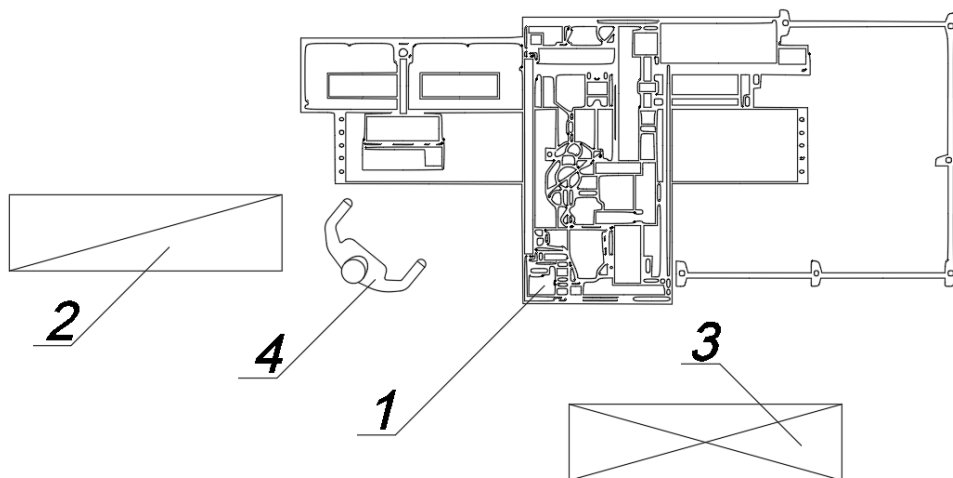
Організація робочого місця біля горизонтального свердлильно-присаджувального центру з ЧПК: 1 – свердлильно-присаджувальний центр з ЧПК, 2 – підступне місце для деталей до обробки, 3 – підступне місце для деталей після обробки, 4 – оператор.
